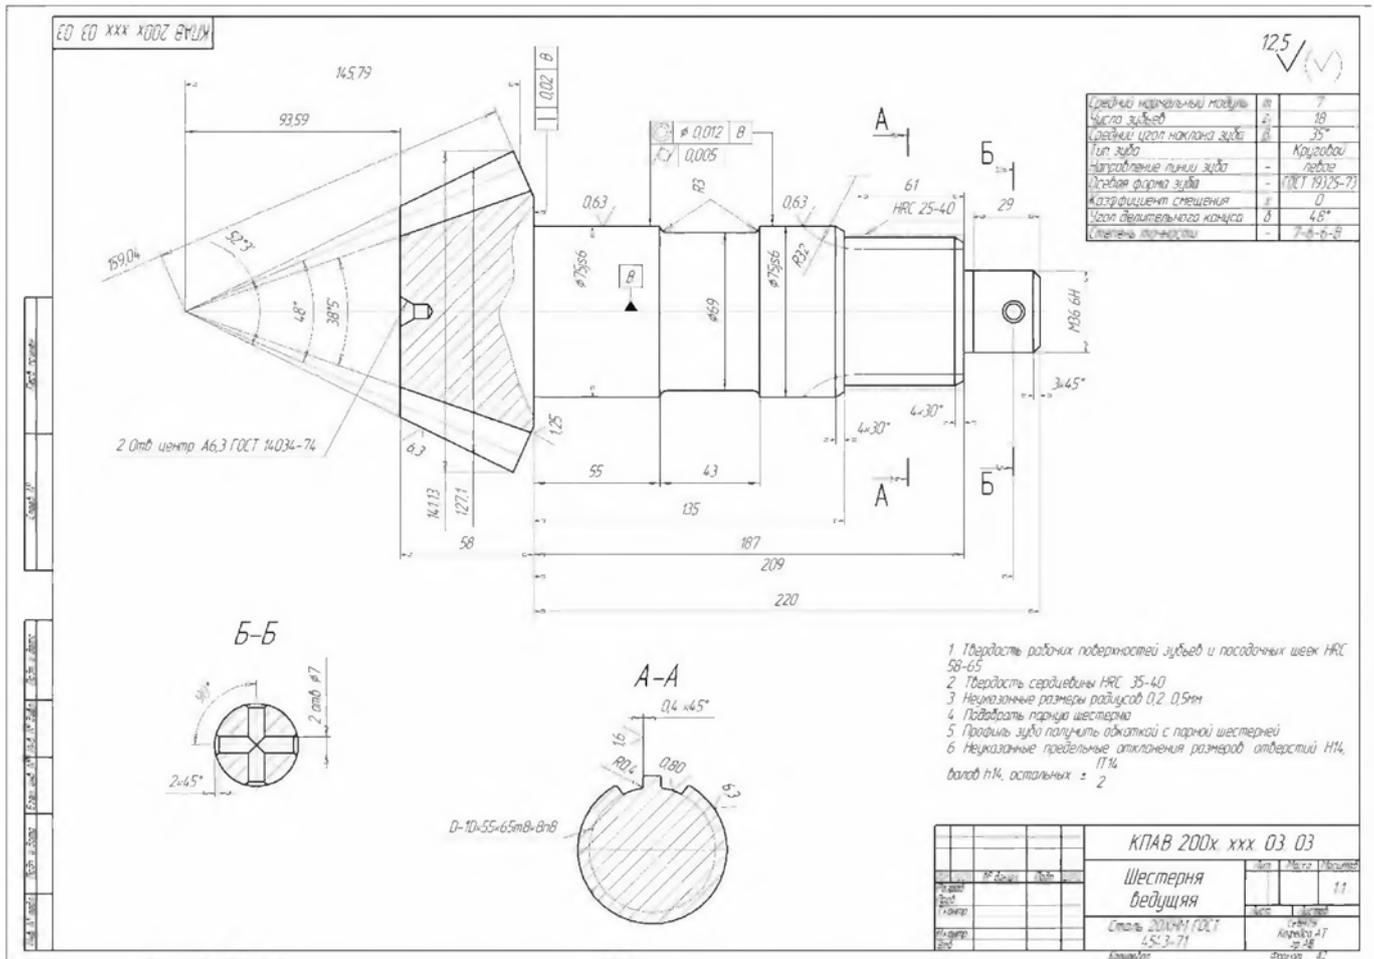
Пример выполнения рабочего чертежа детали.
